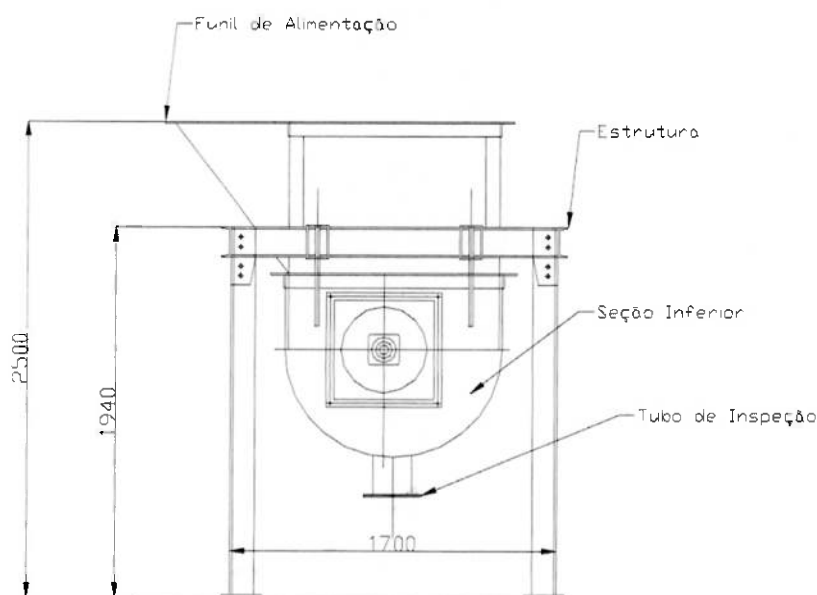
Detalhe da seção inferior do elevador com o funil de alimentação, montada sobre a estrutura
